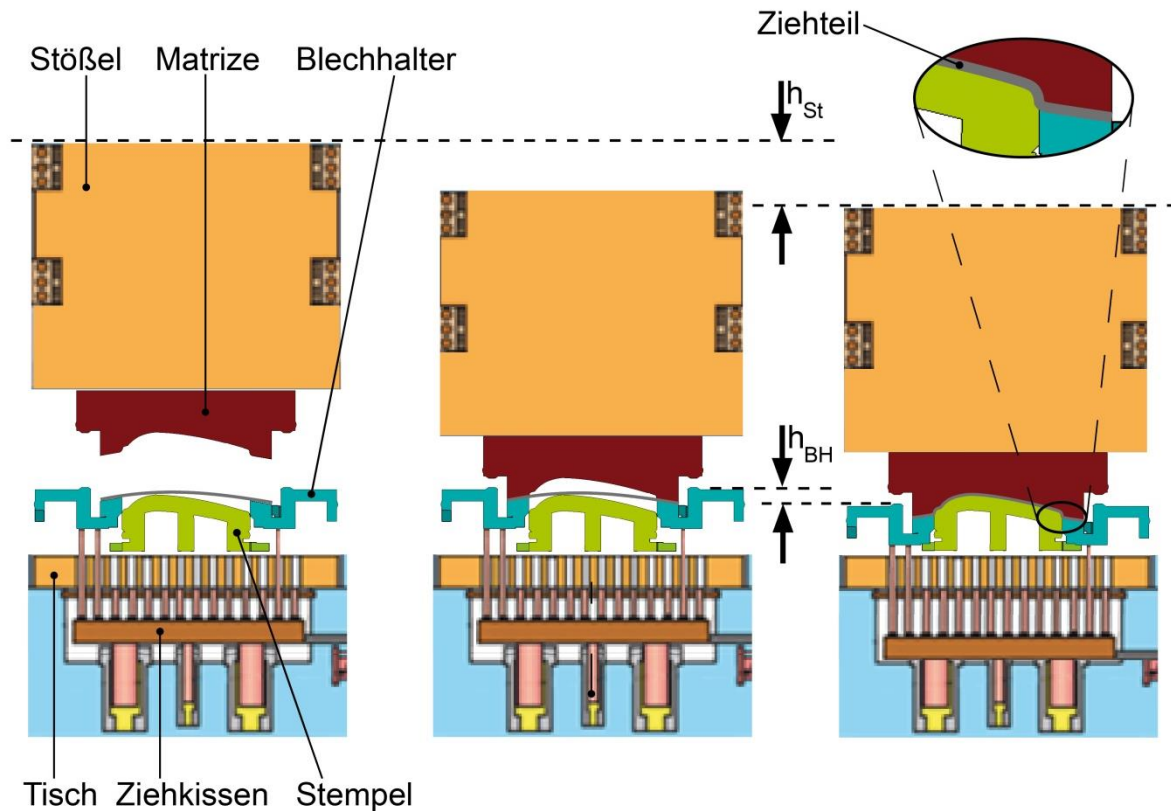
Funktionsprinzip Tiefziehwerkzeug: links geöffnetes Werkzeug, Mitte Blechhalter schließen, rechts Werkzeug in UU
